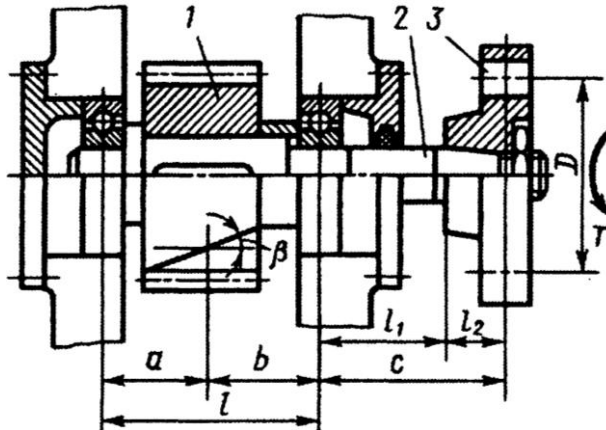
Вал с элементами, расположенными на нем: 1 – шестерня; 2 – вал; 3 – полумуфта
